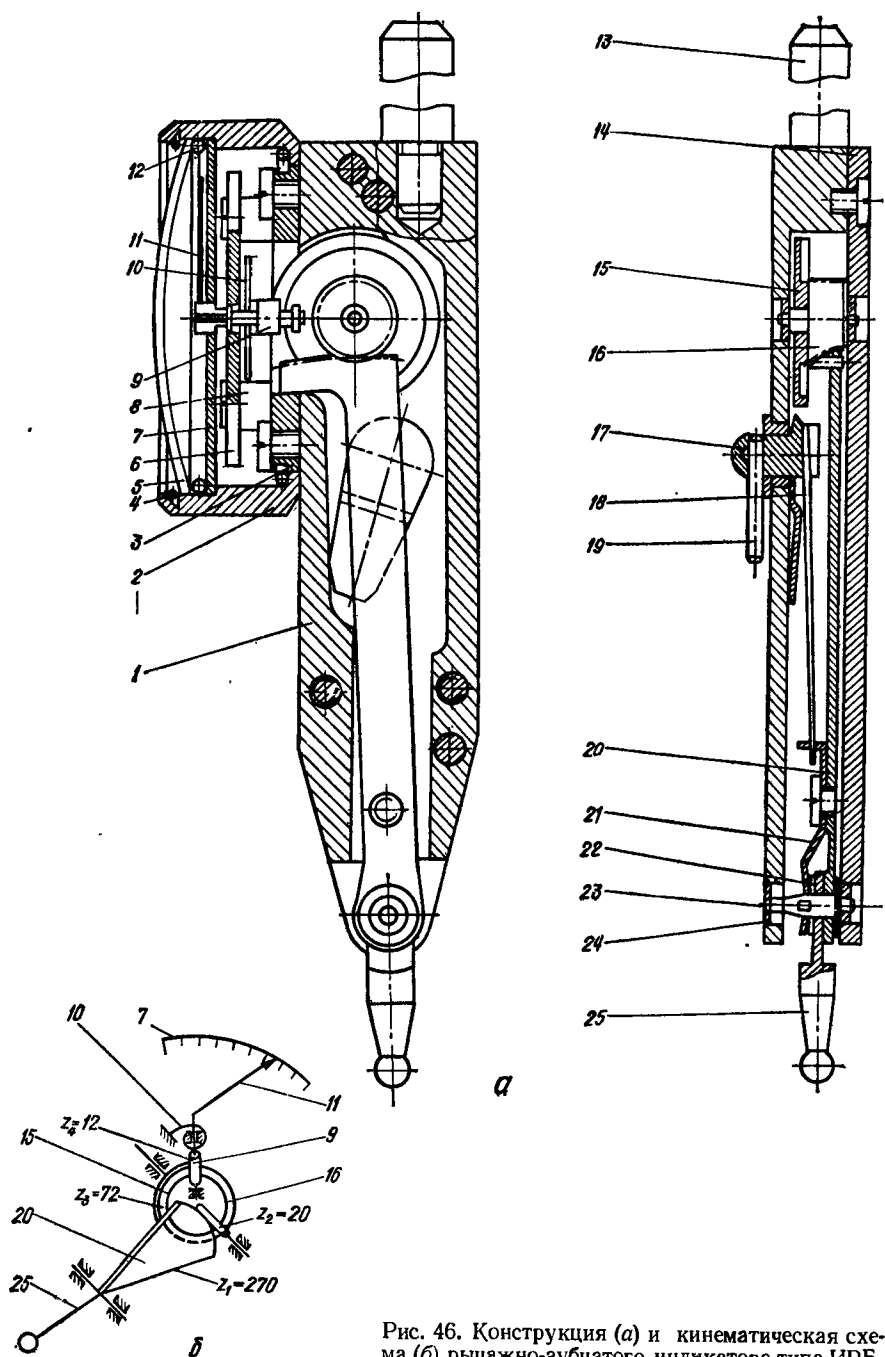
Конструкция (а) и кинематическая схема (б) рычажно-зубчатого индикатора типа ИРБ.
